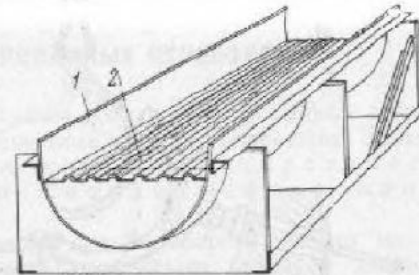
Кондуктор для сборки и сварки комингсов легких дверей.
